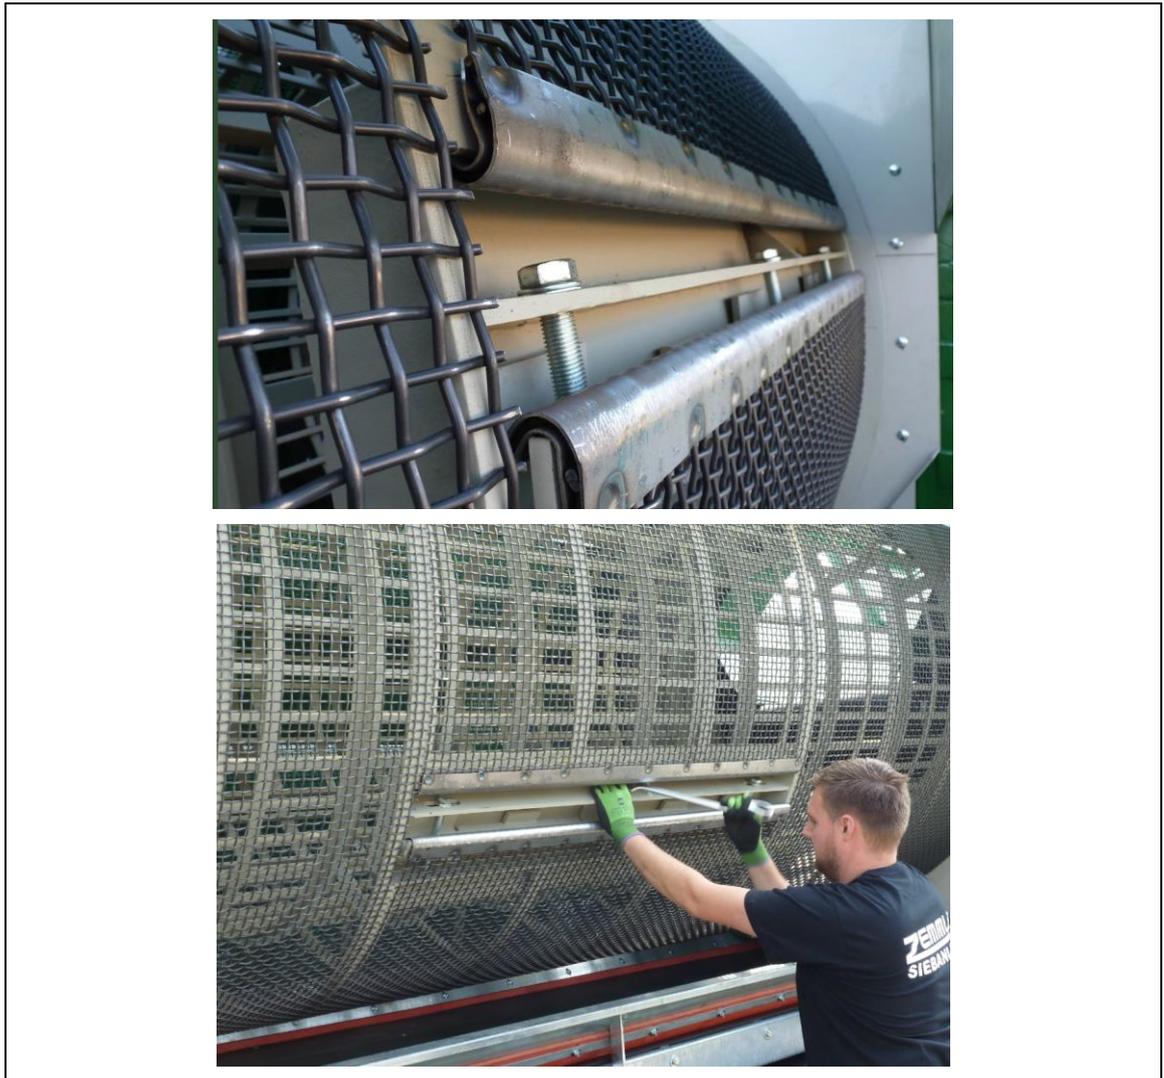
Dispositivo di tensionamento e di fissaggio per la rete della griglia del vaglio
